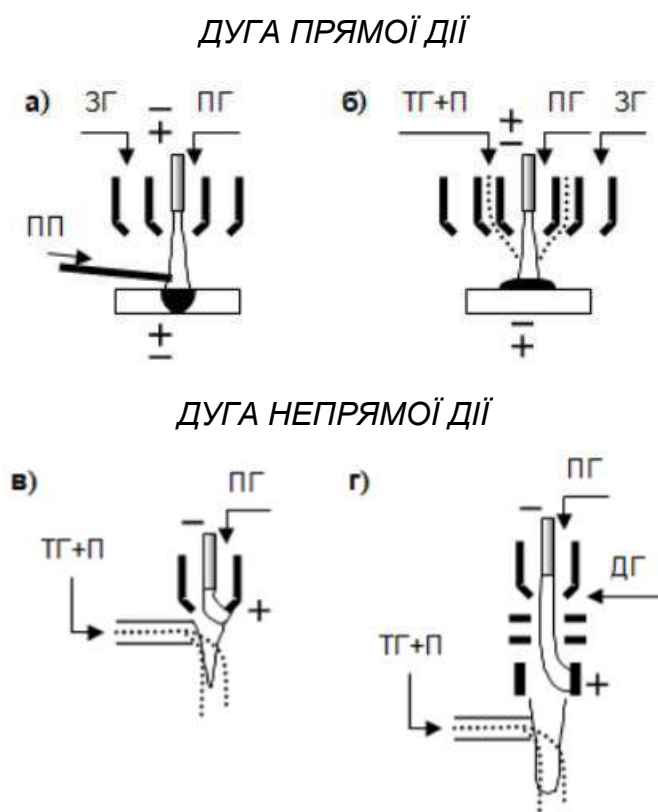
Схеми плазмотронів для зварювання (а), наплавлення (а, б), напилення (в, г), фінішного плазмового зміцнення (г), загартування (а – без ПП):
